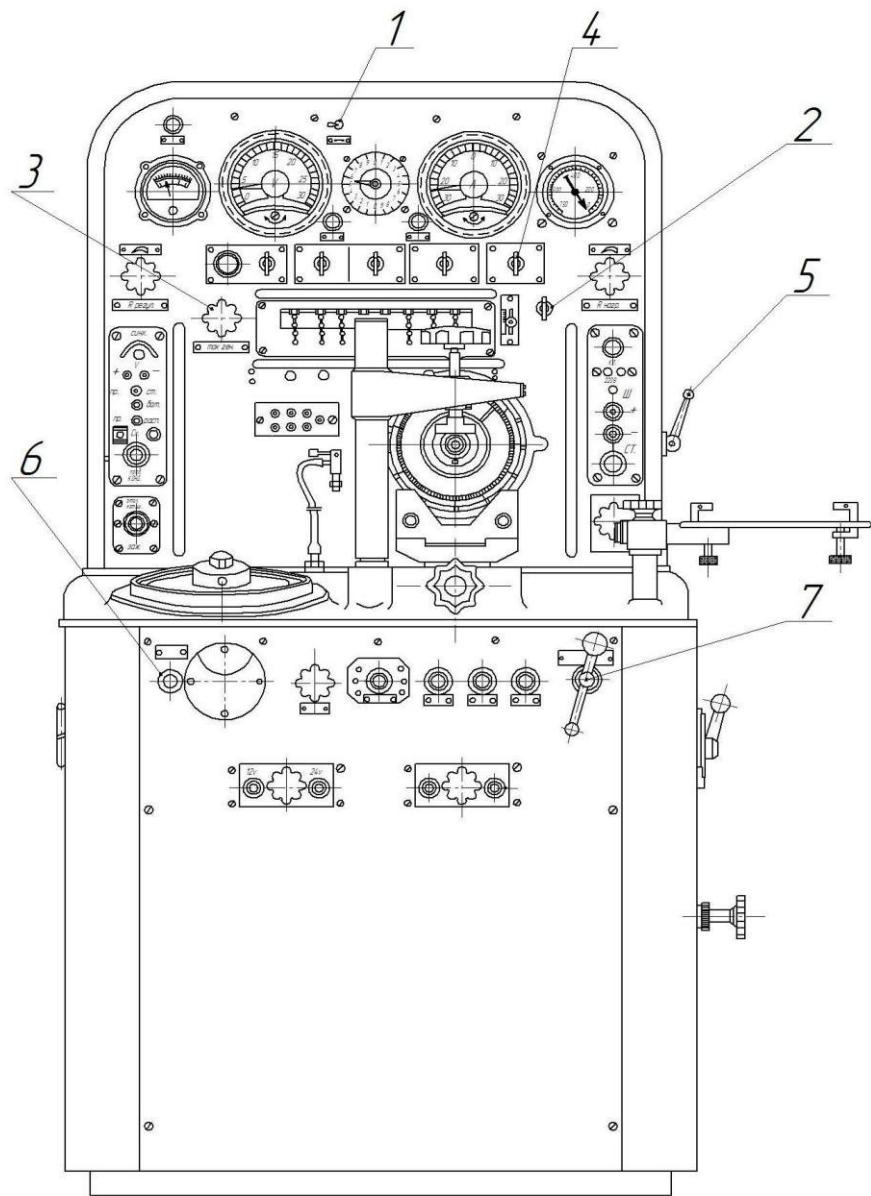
Универсальный контрольно-испытательный стенд КИ-968М:
